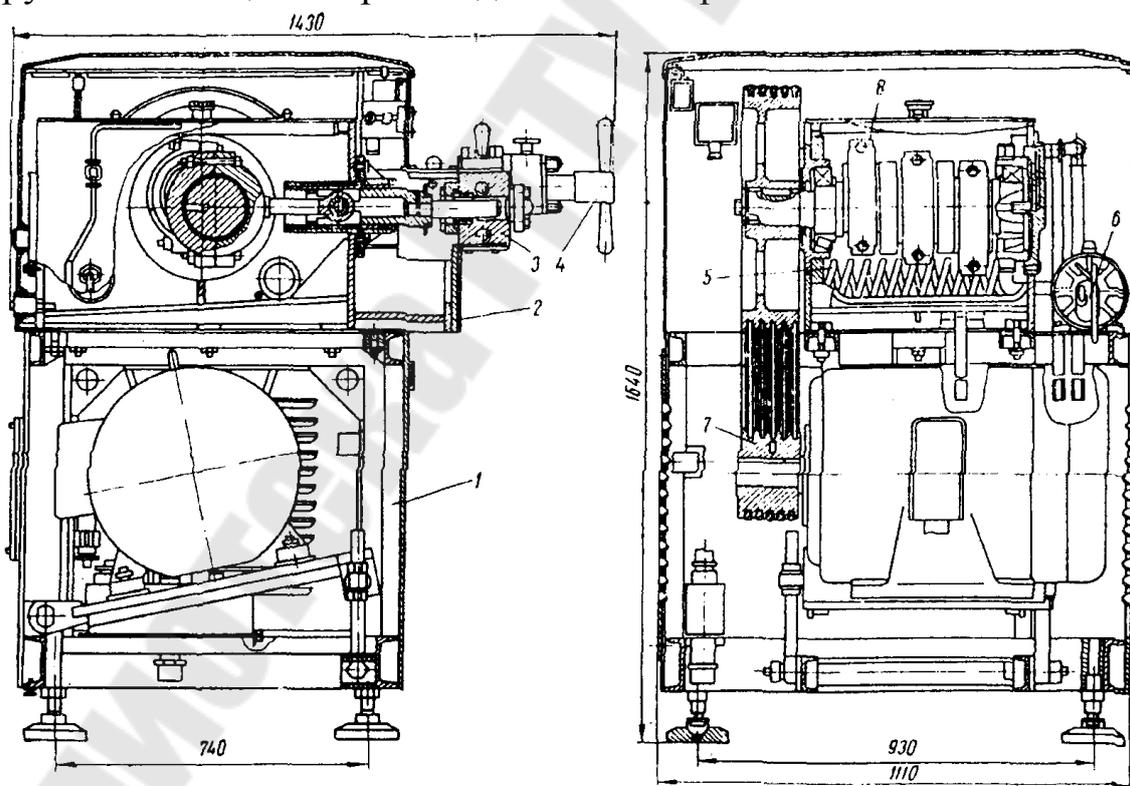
Гомогенизатор: 1 - станина; 2 - корпус; 3 - плунжерный блок; 4 - гомогенизирующая головка; 5 - система охлаждения; 6 - система смазки; 7 - привод; 8 - кривошипно-шатунный механизм.
